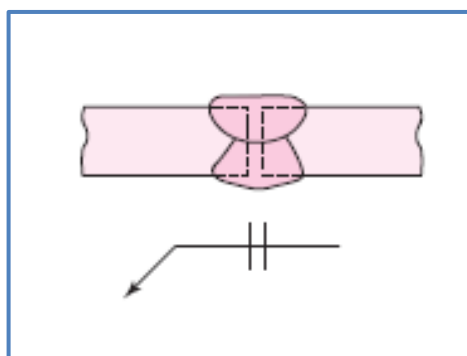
Soldadura a tope con ambos lados rectos
